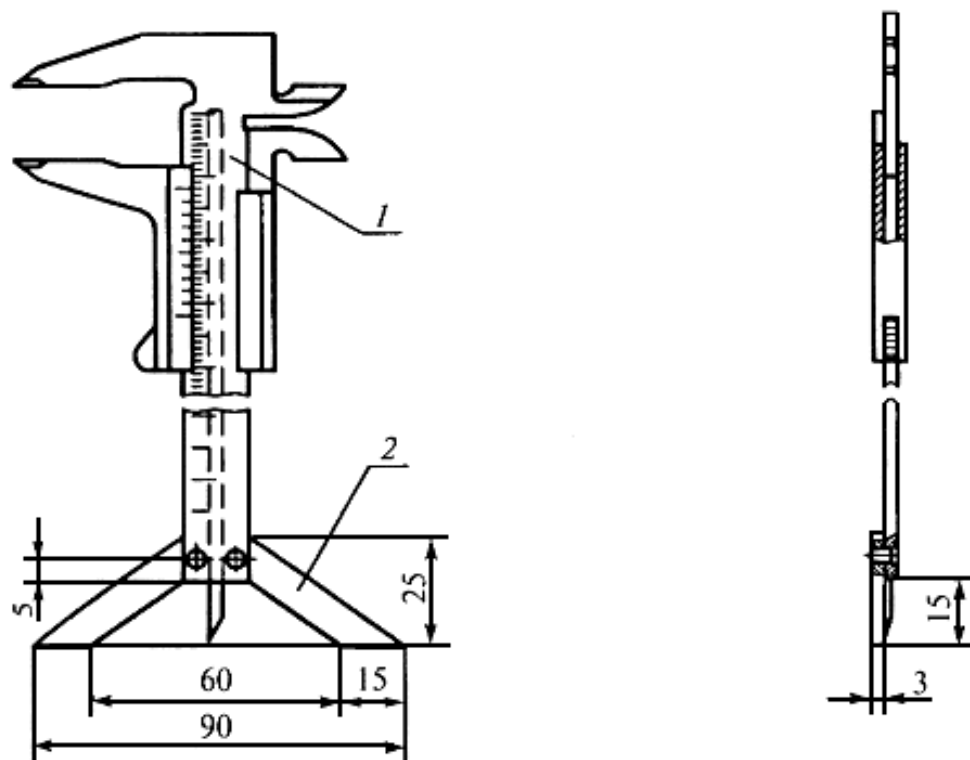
Штангенциркуль типа ШЦ-1 с опорой
